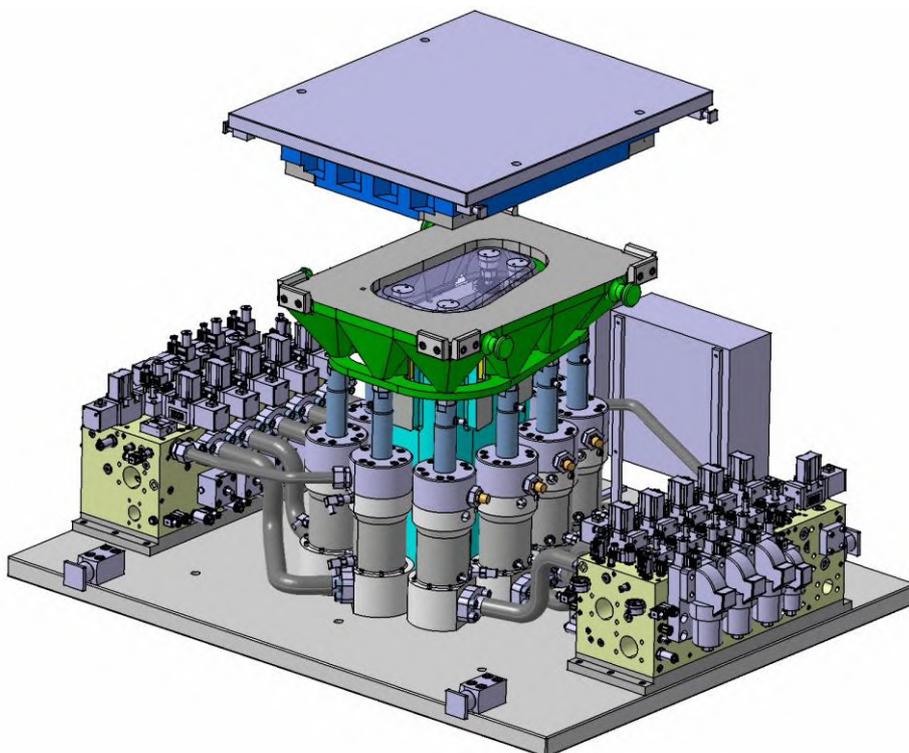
Versuchswerkzeug mit Segmentelastischem Blechhalter und in das Werkzeug integrierter Zieheinrichtung [6]
